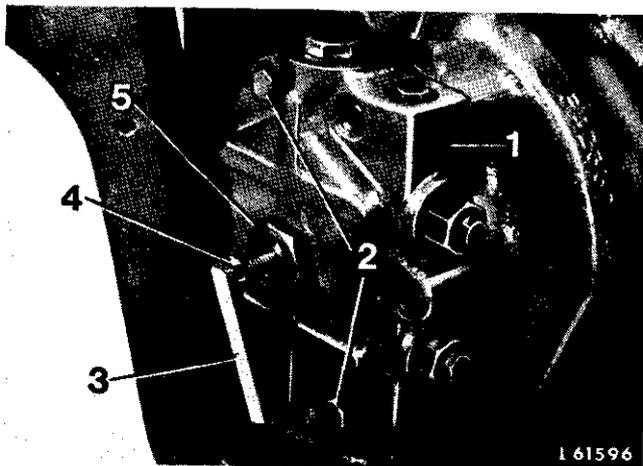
Equipement pour mesurer le jeu axial de l'arbre d'un moteur hydraulique
